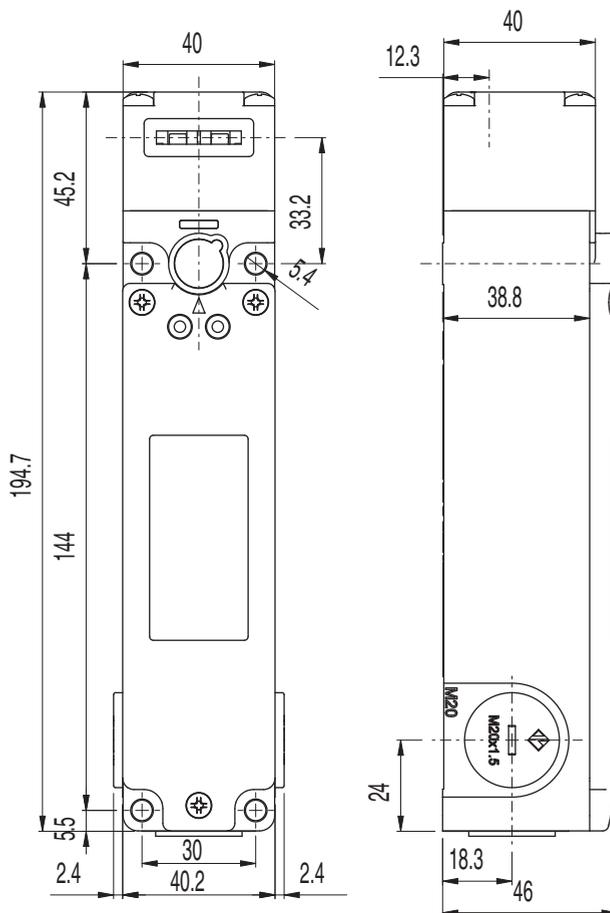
Dimensões do L200-M1C3-MLM24-L2G em mm
